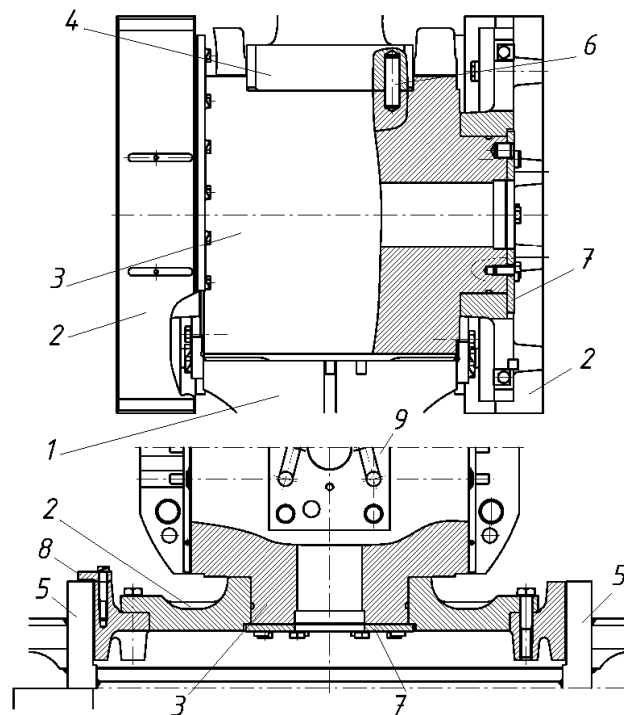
Крейцкопф і його елементи. 1 – шатун; 2 – повзун; 3 – поперечка; 4 – шток поршня; 5 – паралелі; 6 – установочний штифт; 7 – фіксуючі кришки; 8 – бічні опорні планки, 9 – привалочна поверхня поперечки
